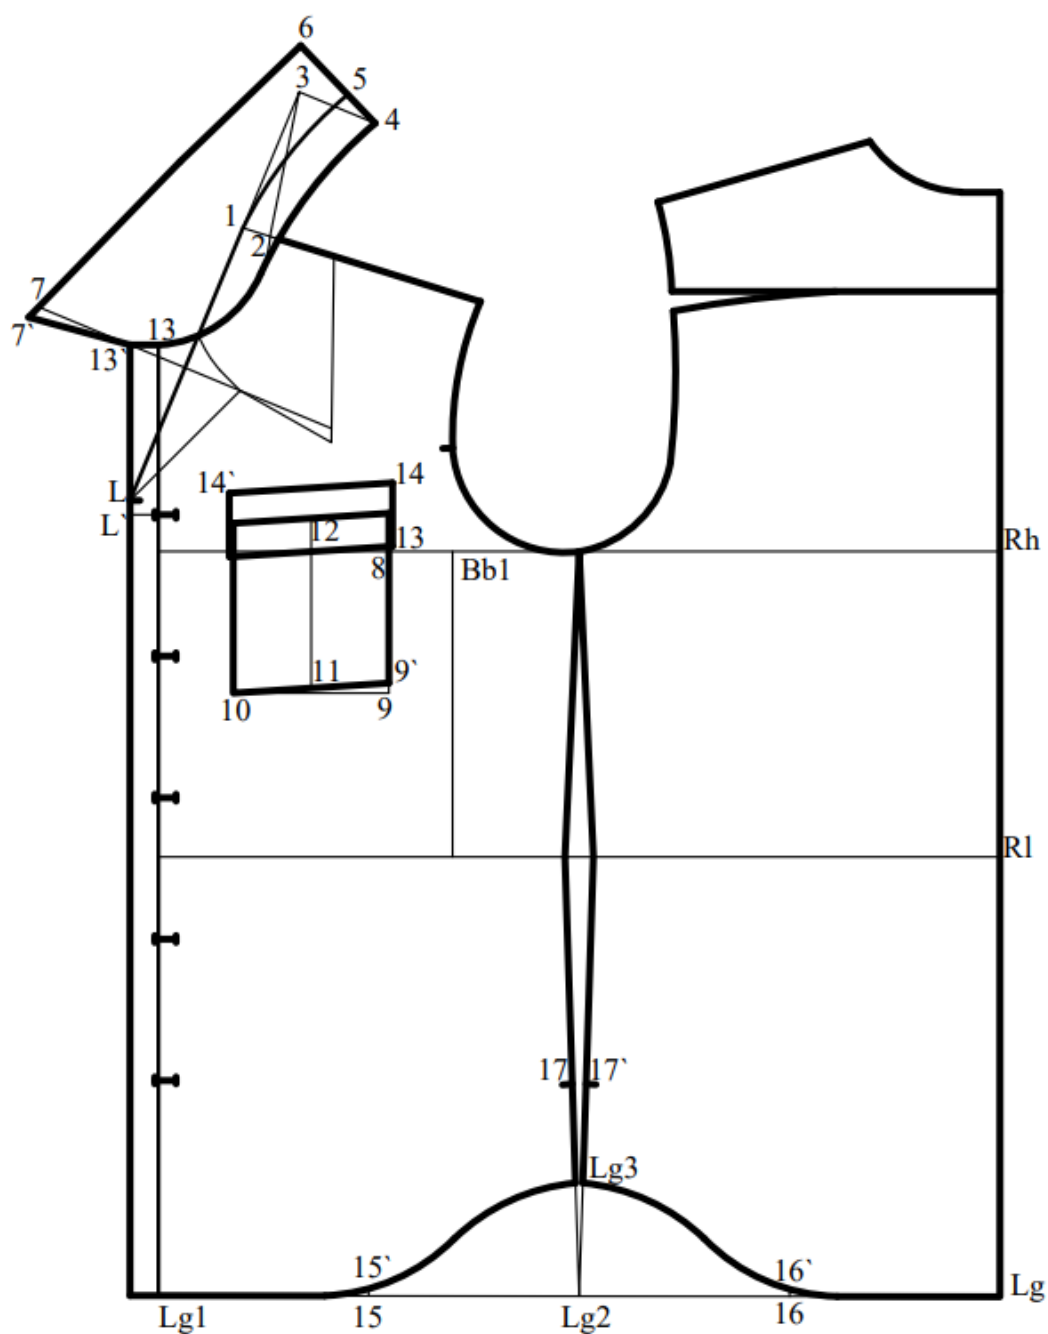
Чертёж модельной конструкция спинки и переда, воротника мужской сорочки
